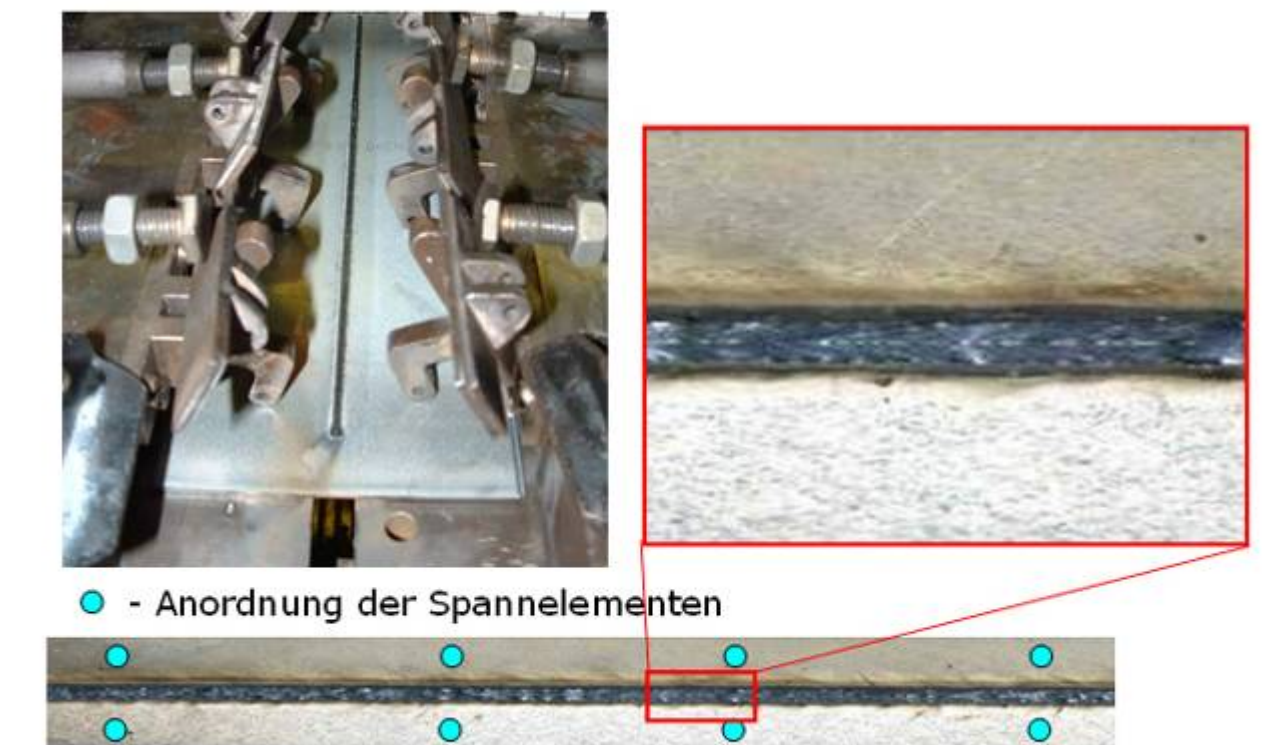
Einzelne punktförmige Spannbacken (acht Spannelemente)
